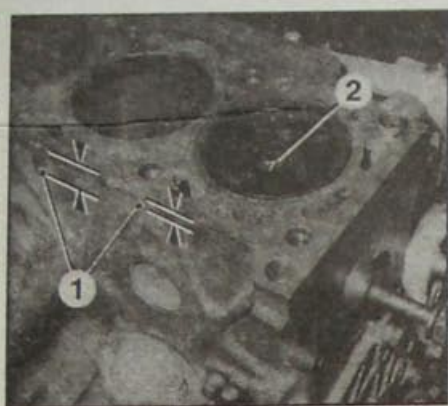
Маркировка диаметра цилиндра на блоке цилиндров:
